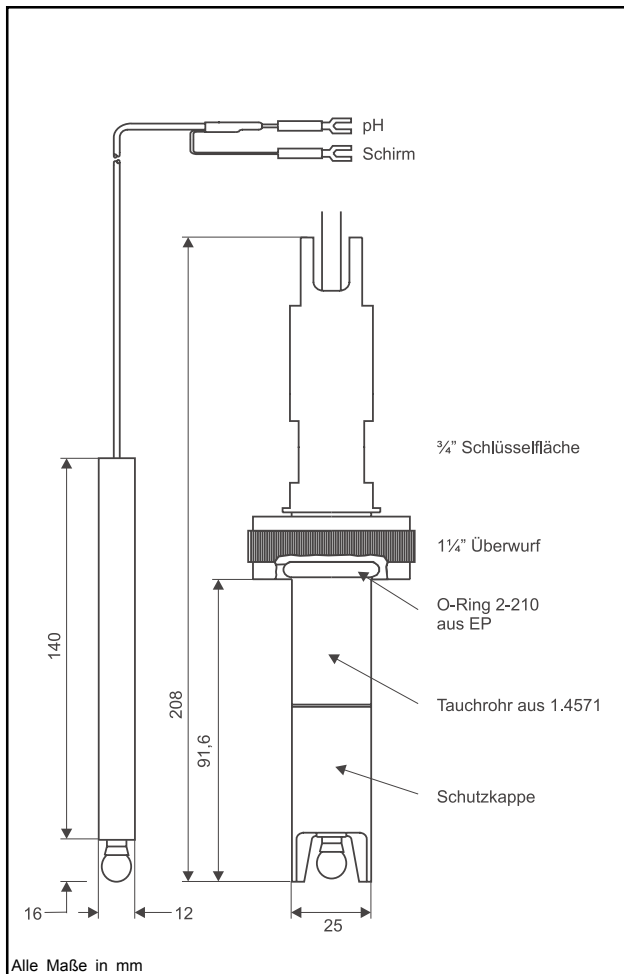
Mechanische Abmessungen Sensor Modell 328A und Montageadapter P/N 22294-00
